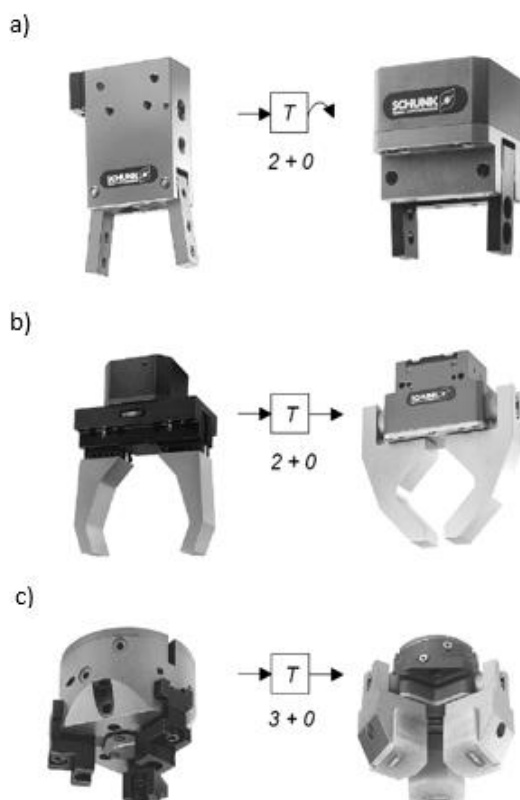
Chapadla s pneumatickým pohonem, zdroj: <http://www.robot27.com/contact/>
